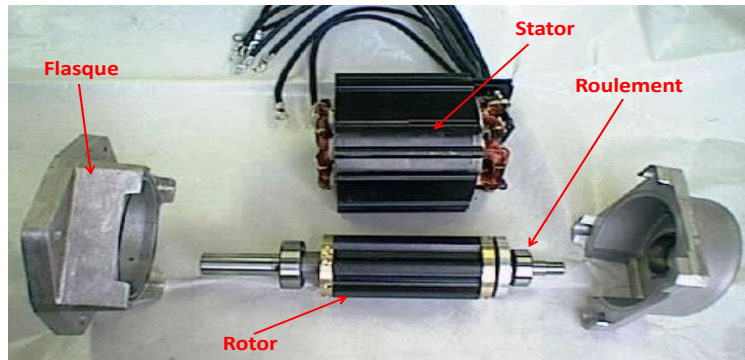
Vue éclatée de la machine à réluctance variable [77].
